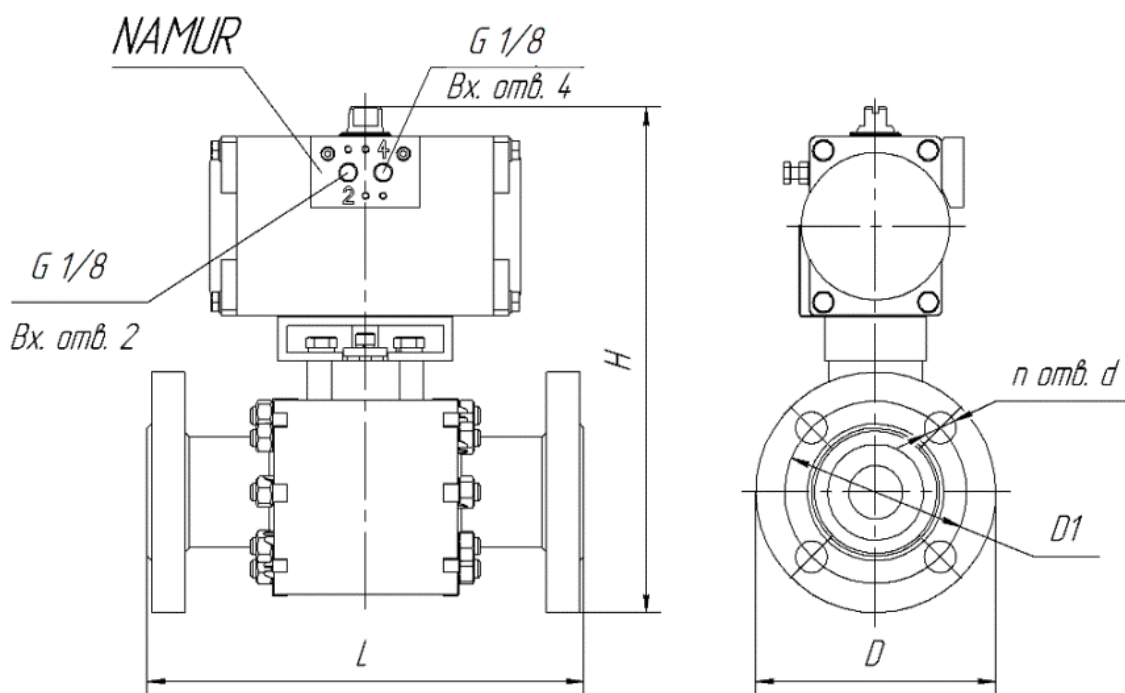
Габаритный чертеж устройства РУС-Ш без пускового узла
